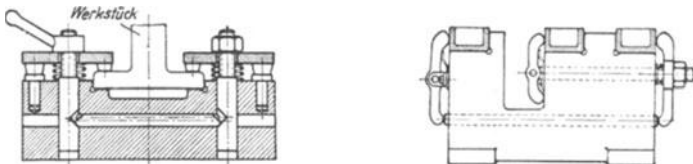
Befestigen mehrerer Spanner oder Werkstücke durch ein Spannelement.
